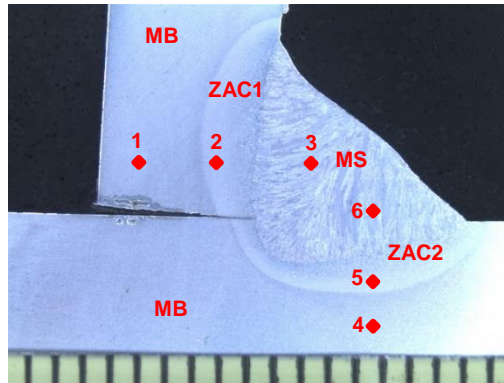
Zonas indentadas en la unión soldada. MS, MB, ZAC1 y ZAC2
